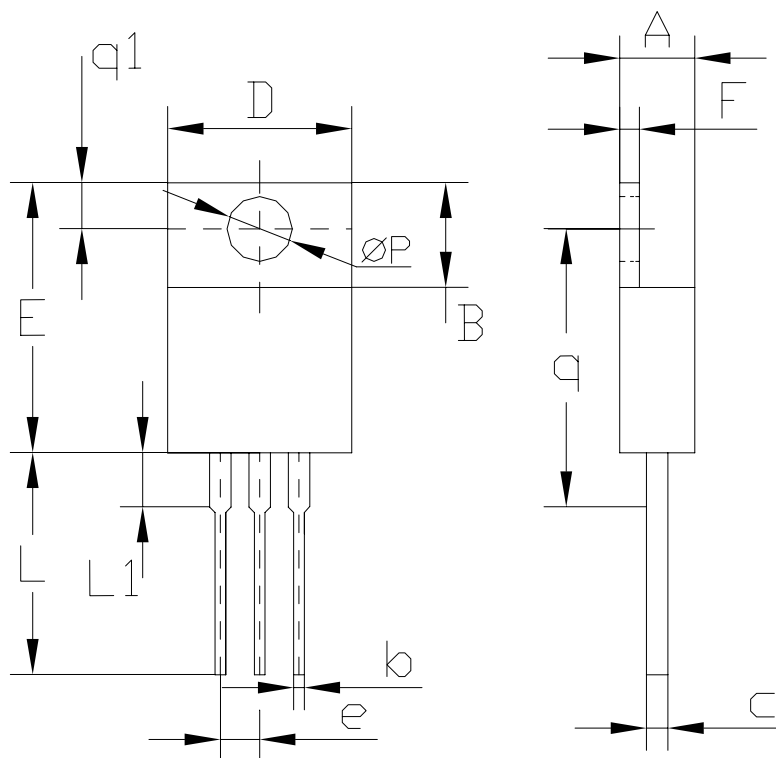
Габаритный чертеж корпуса КТ-89 (DPAK)
